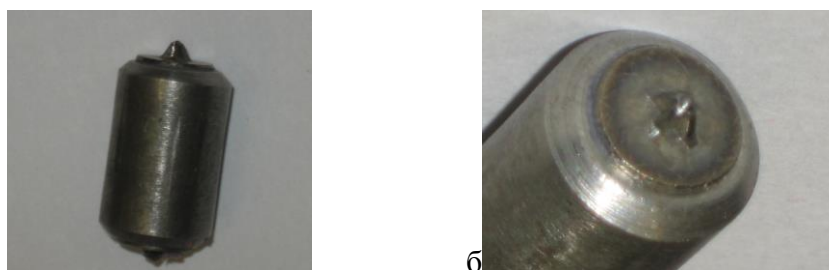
Общий вид (а) и рабочая часть (б) отделочного пуансона для изготовления винтов-саморезов
